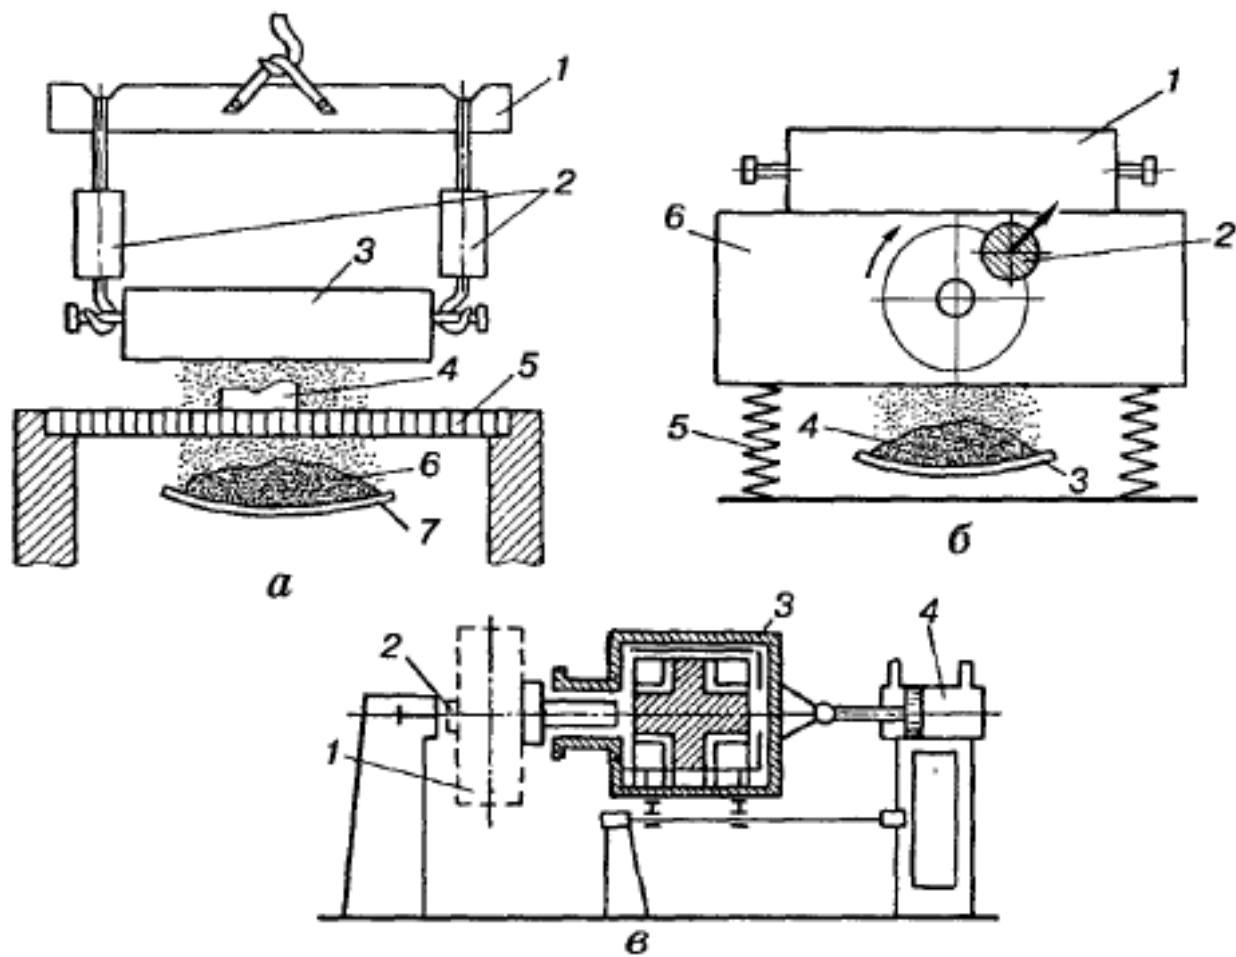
Схеми пристроїв для вибивання форм і стрижнів
